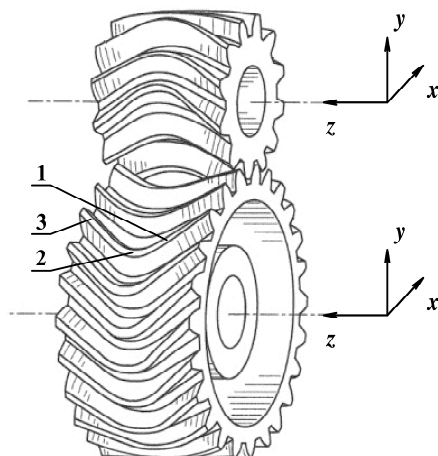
Циліндрична евольвентна передача з арково-гвинтовими зубцями:
